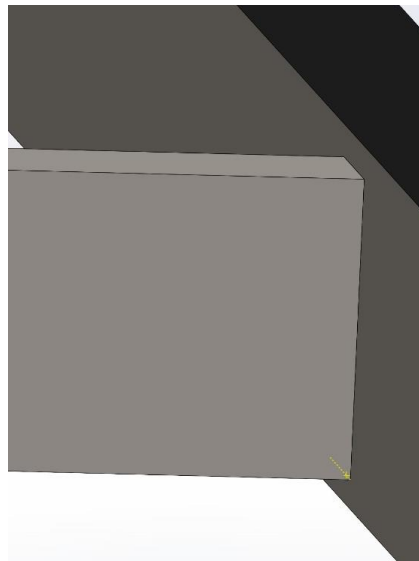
Análisis del Cordón de soldadura del lado inferior del perfil
